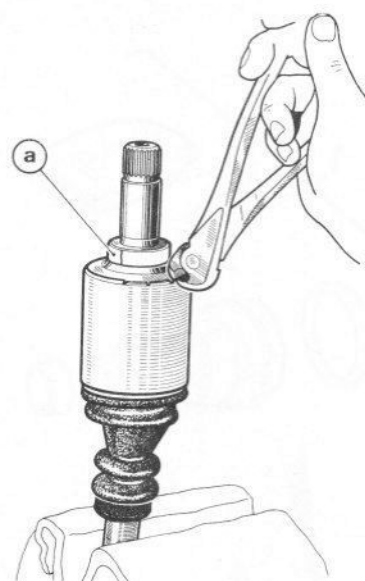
Desserrer le capot en tôle du joint d'arbre de roue (Sec 5)
